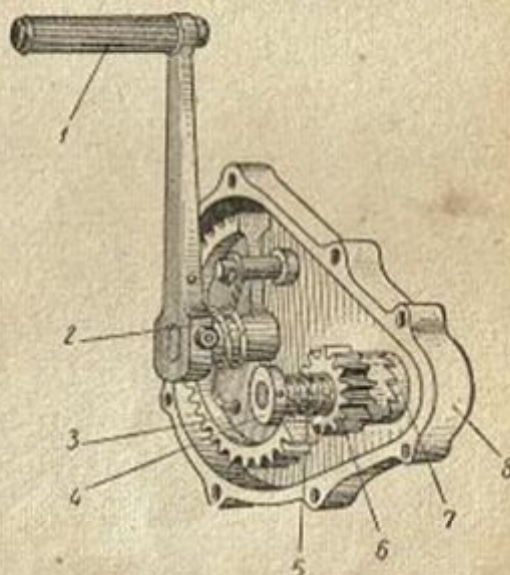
Пусковой механизм, имеющий храповую шестерню с зубчатым сектором:
